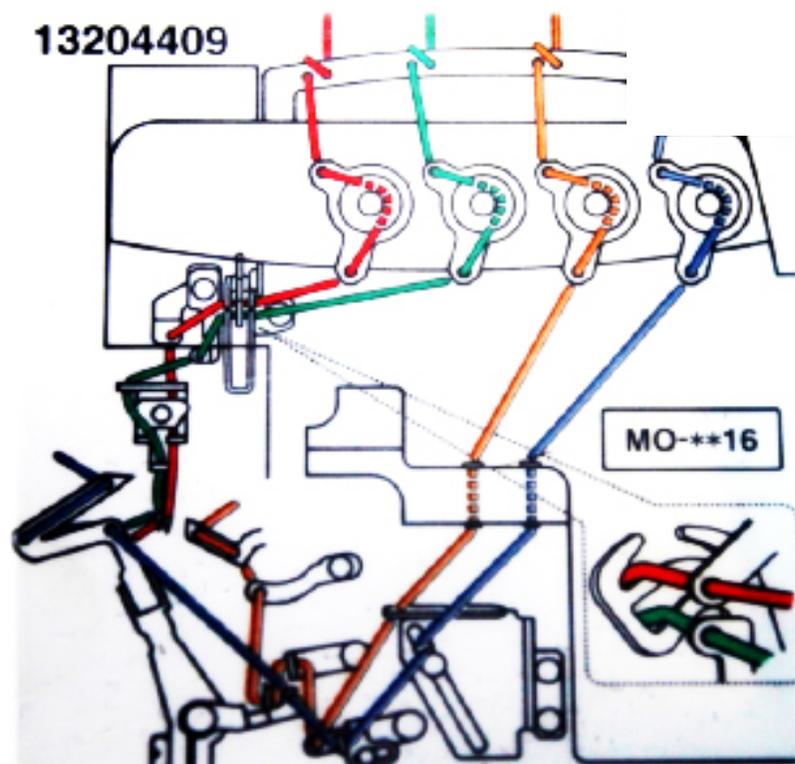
Enhebrado interno de la máquina industrial overlock. Fuente: Autoría propia.
